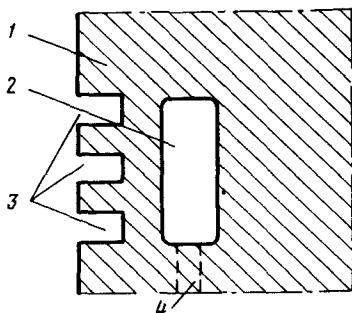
Алюминиевый поршень дизеля Д70 с охлаждением зоны установки поршневых колец
